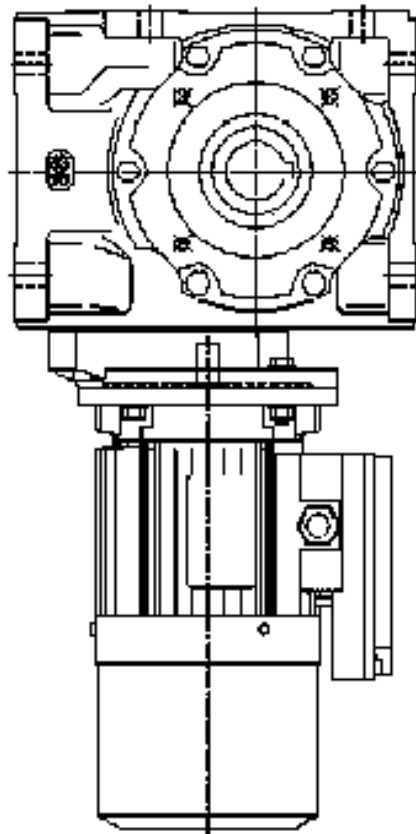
Мотор-редуктор Rossi motoriduttori 71с6
